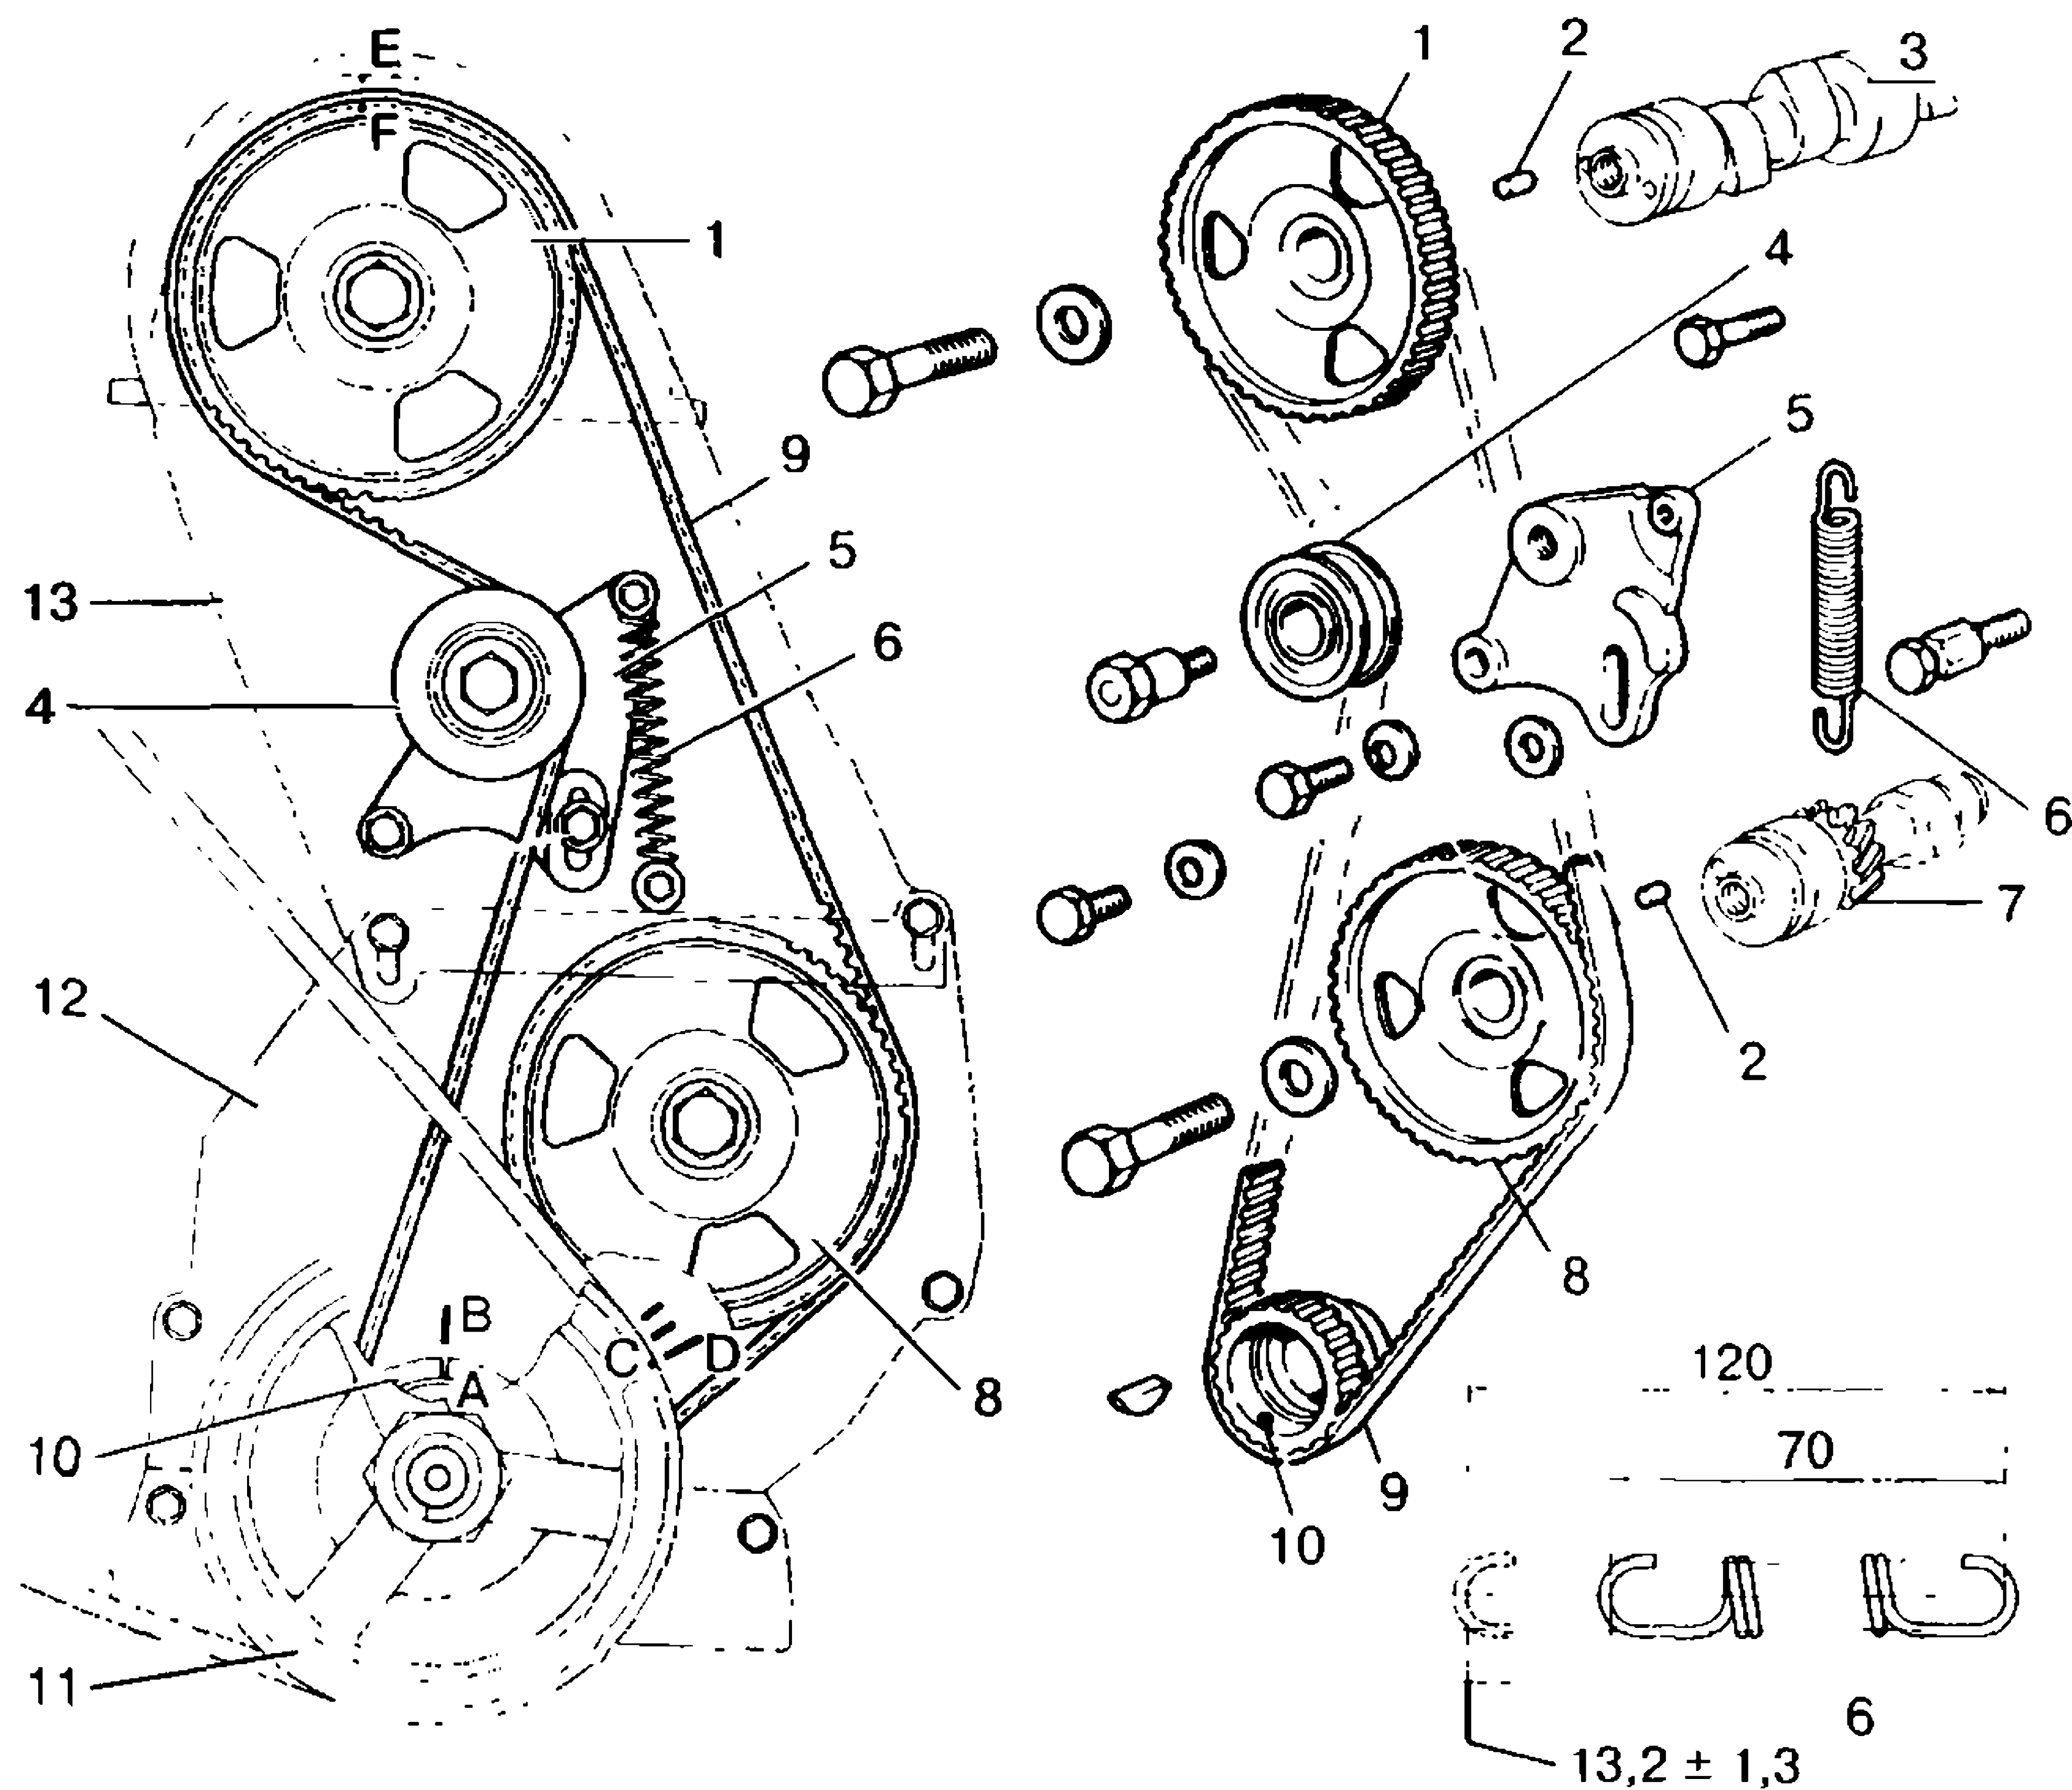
Ременный привод распределительного вала двигателя 2105:
